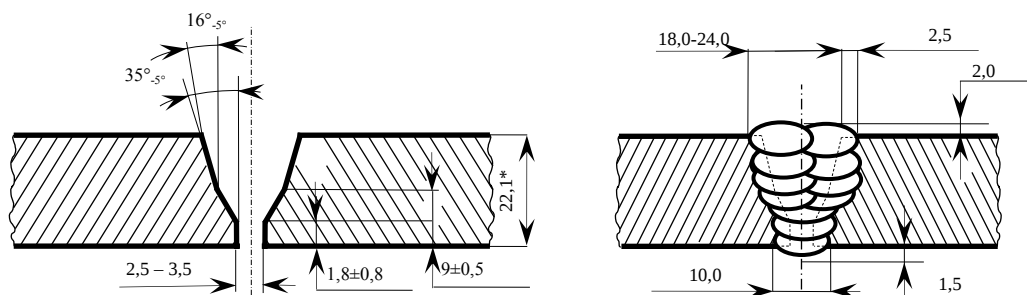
Геометрические параметры сборки и сварного шва КСС №1, 2
